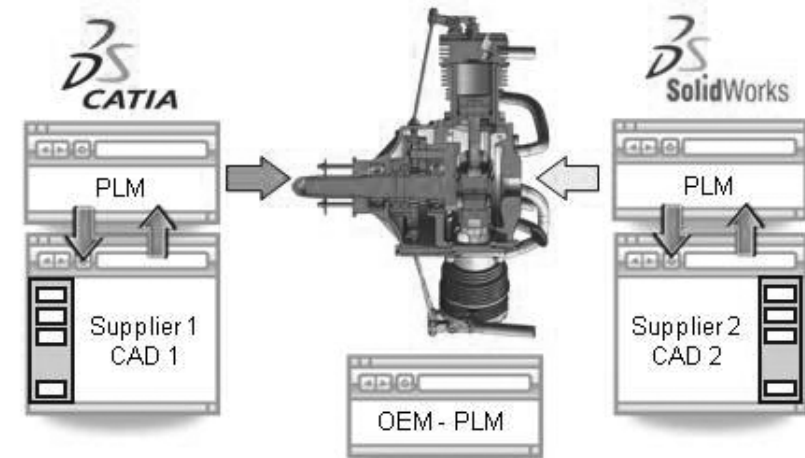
Aufbau einer beispielhaften, heterogenen Assembly
